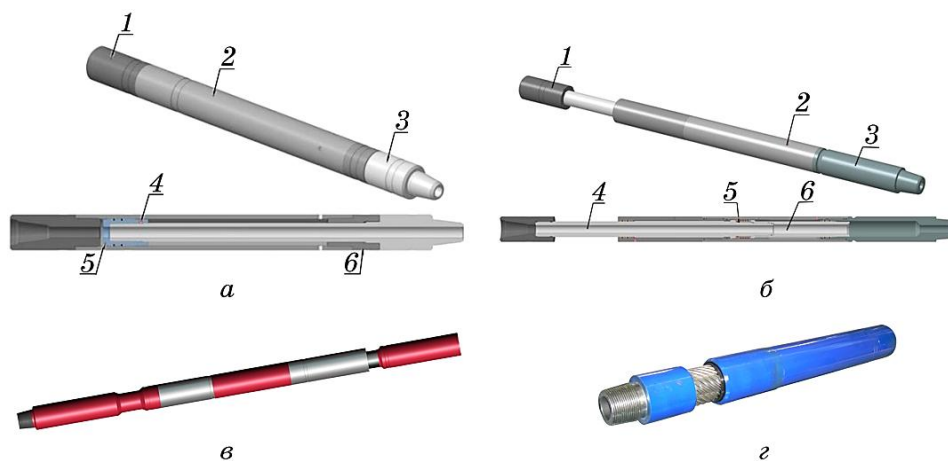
Яс: *a* — механічний (1 — корпус верхній, 2 — корпус, 3 — шток, 4 — шпеник, 5 — хвостовик штока, 6 — корпус нижній); *б* — гідравлічний (1 — перевідник, 2 — корок, 3 — корпус, 4 — шток, 5 — поршень, 6 — хвостовик штока); *в* — гідравлічний з'єднанням у стик з накладками із буравленням, *г* — крутильний «Shock Turn».
